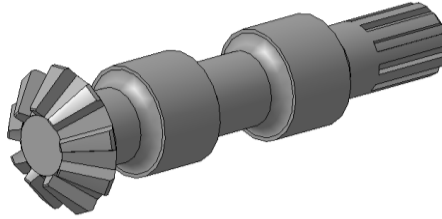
Заокруглення поверхонь шестерні головної передачі
